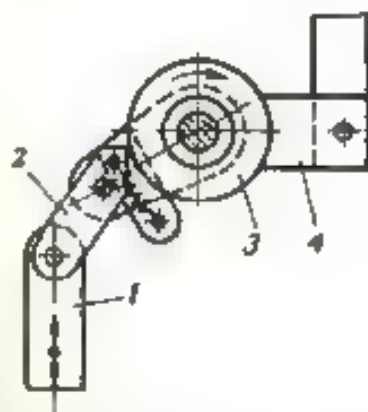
Západkový podávací mechanismus s obousměrnou blokovací záradkou pro posuv papíru o řádkovou mezenu u psacího stroje
